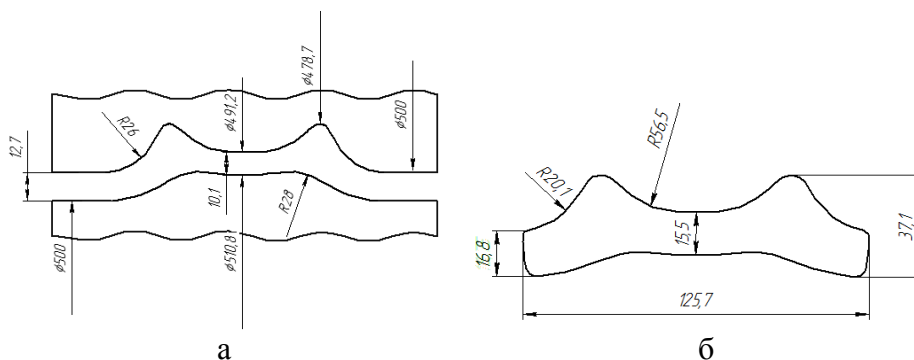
Экспериментальные исследования напряженно-деформированного состояния при прокатке швеллера: а – размеры формообразующего калибра; б – форма и размеры заготовки
